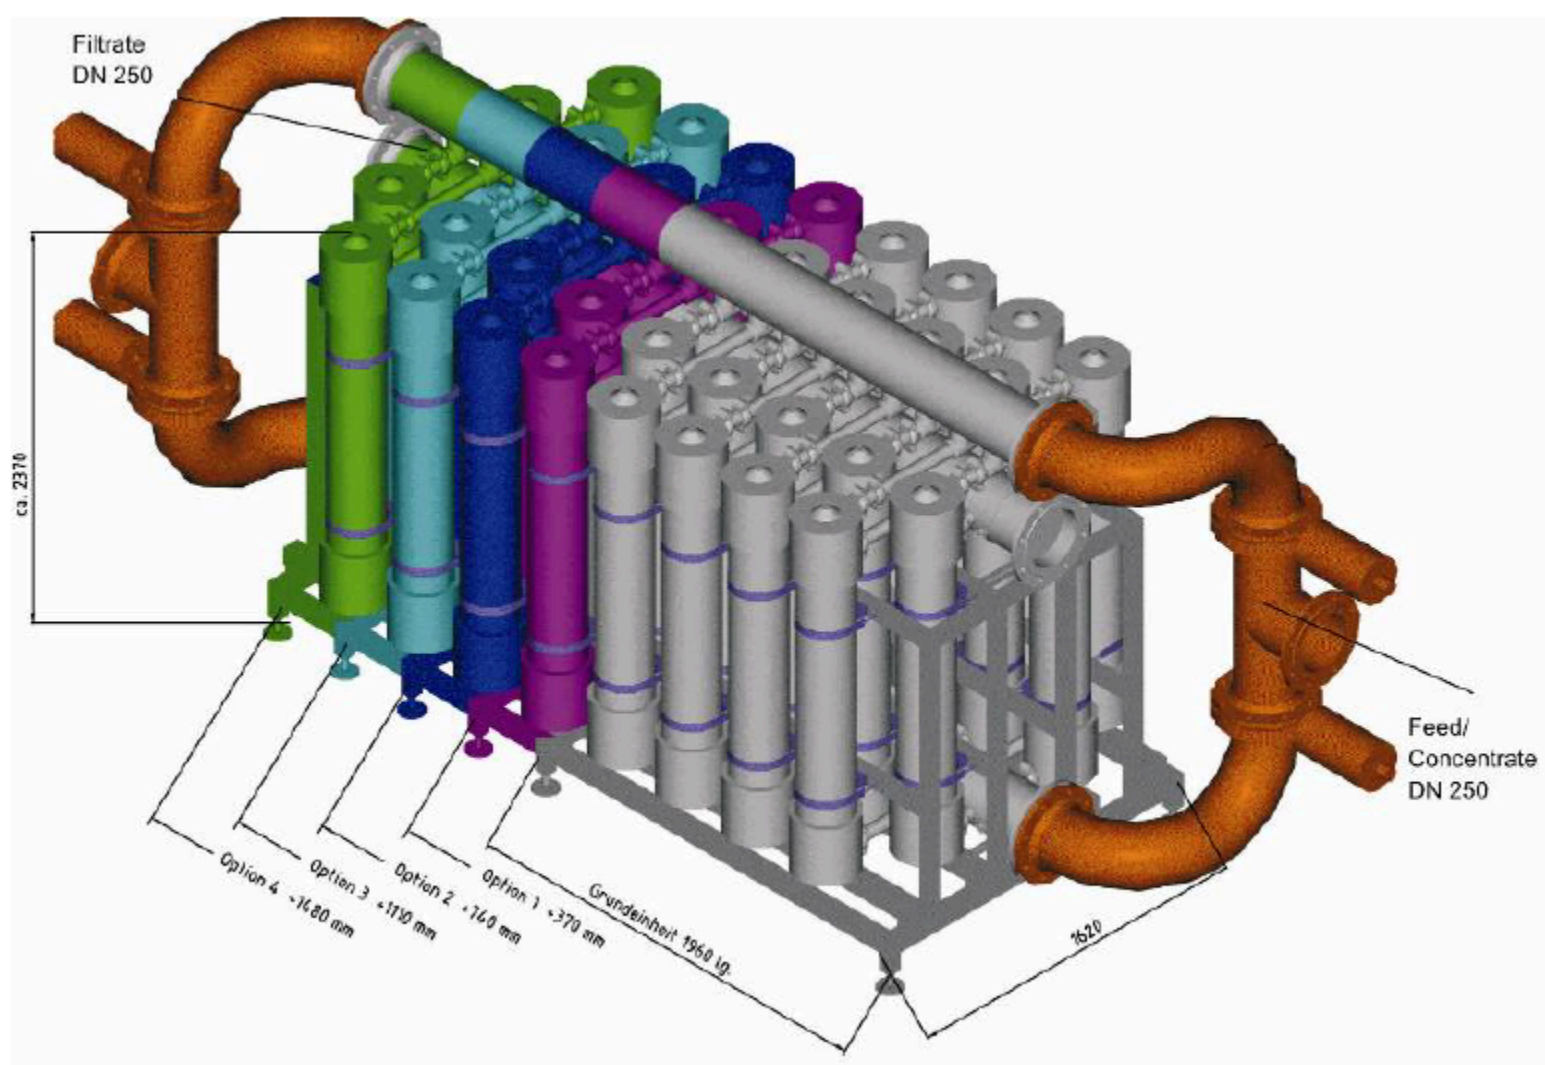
Типичная конструкция стойки для 34 модулей dizzer@ с центральным коллектором и двухрядное расположение с каждой стороны
